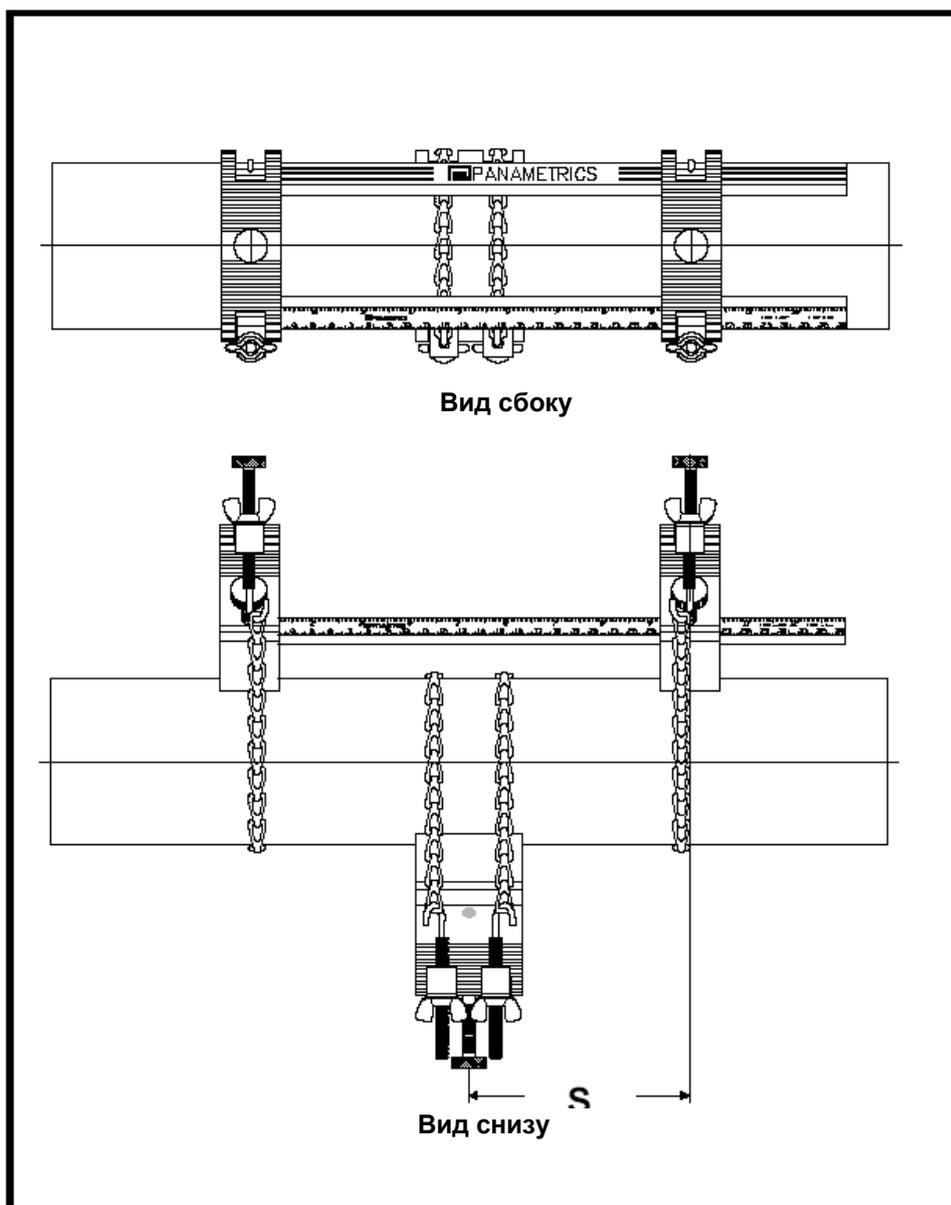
Установка приспособления для одноходового варианта системы в сборе
